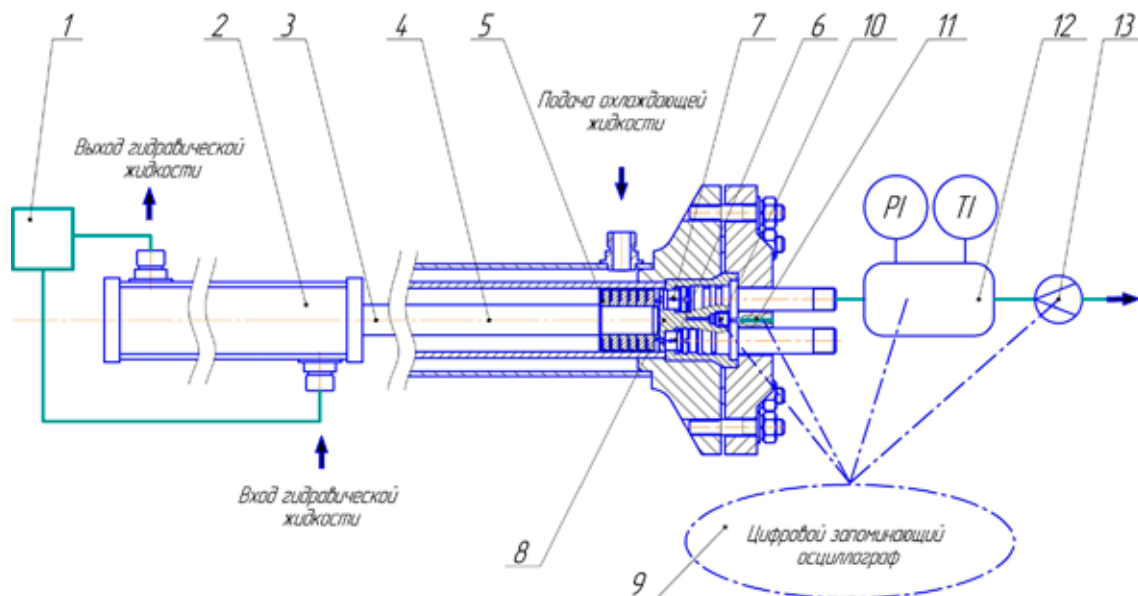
Схема тихоходной длинноходовой ступени поршневого компрессора с линейным гидроприводом:
